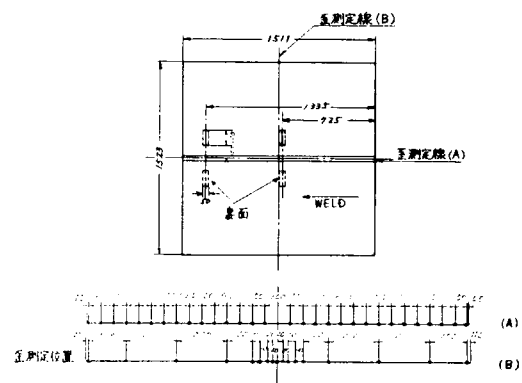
(3) 試験片寸法および測定位置 (KAS 鋼エレクトロslag 溶接継手)
